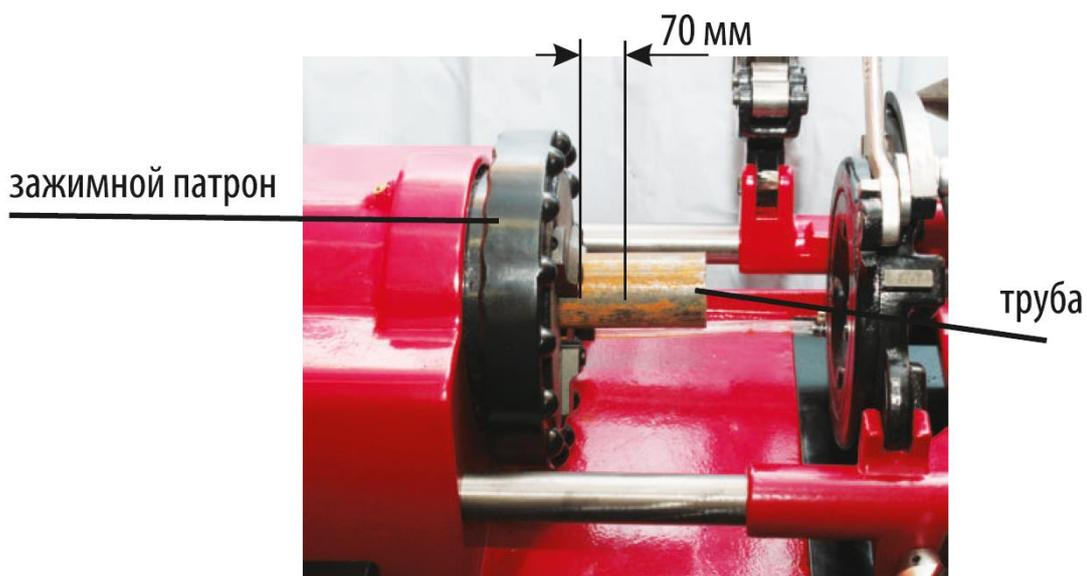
Расстояние между областью резьбы на обрабатываемой детали и зажимным патроном
